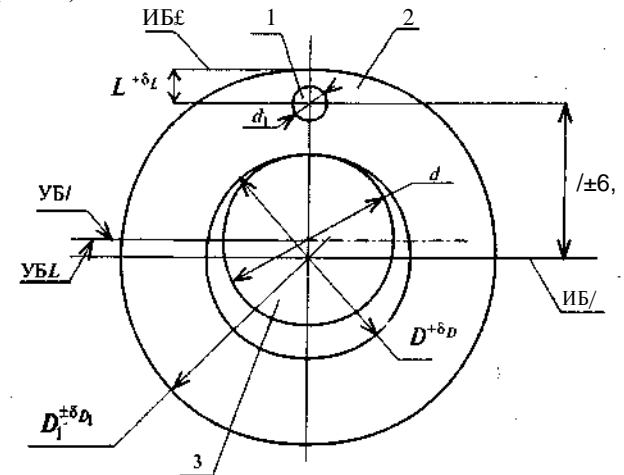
Базирование заготовки на цилиндрическую поверхность
